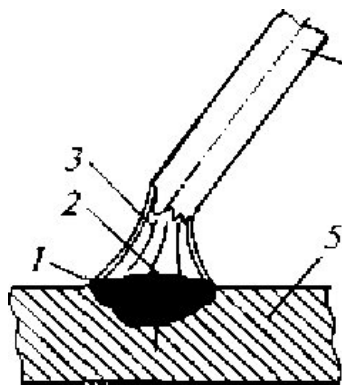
Схема зварювання деталей зварною дугою: 1 - розплавлений метал; 2 - границя розплаву; 3 - електрична дуга; 4 - електрод; 5 – деталь
